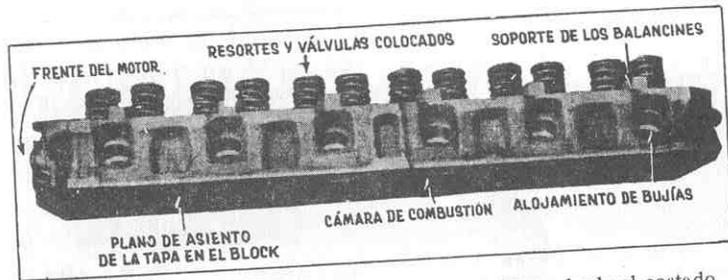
Tapa de cilindros del motor 221 SP. Vista desde el costado izquierdo.
